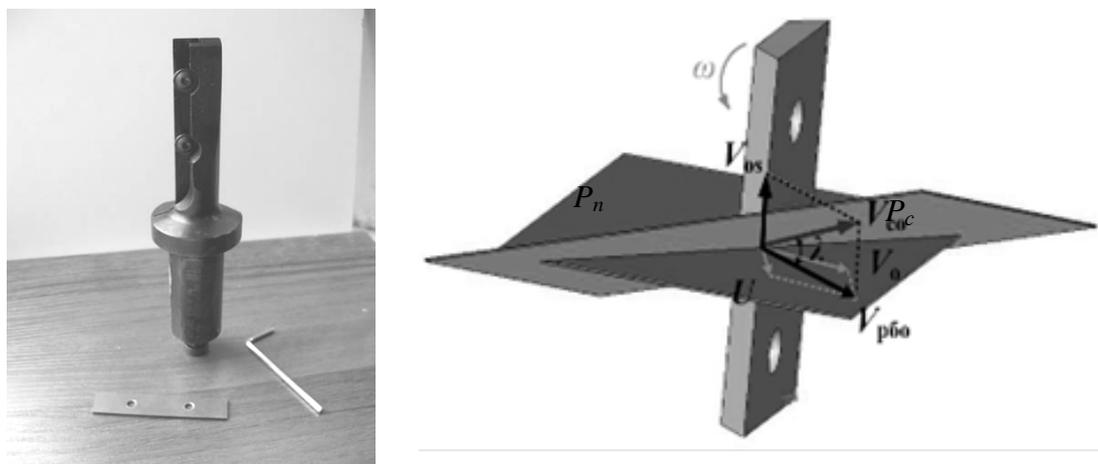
Сборная хвостовая фреза и схема векторов скоростей вращающейся хвостовой фрезы с дополнительным движением вдоль режущей кромки:
